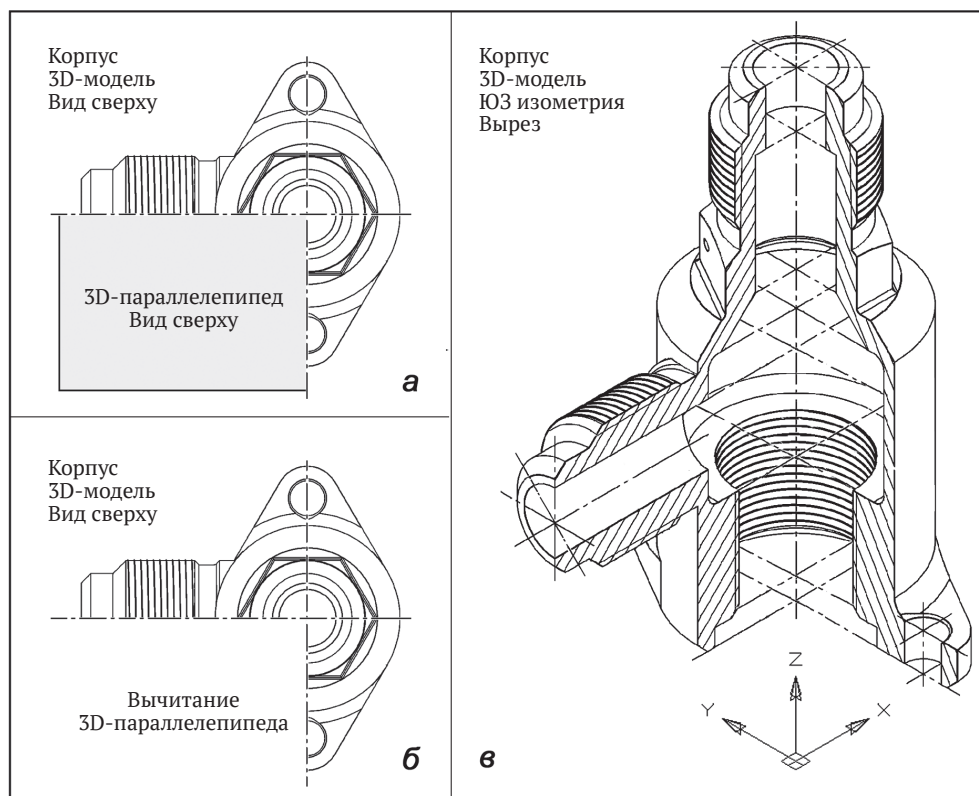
Последовательность выполнения четвертного выреза в 3D-модели детали «Корпус»
